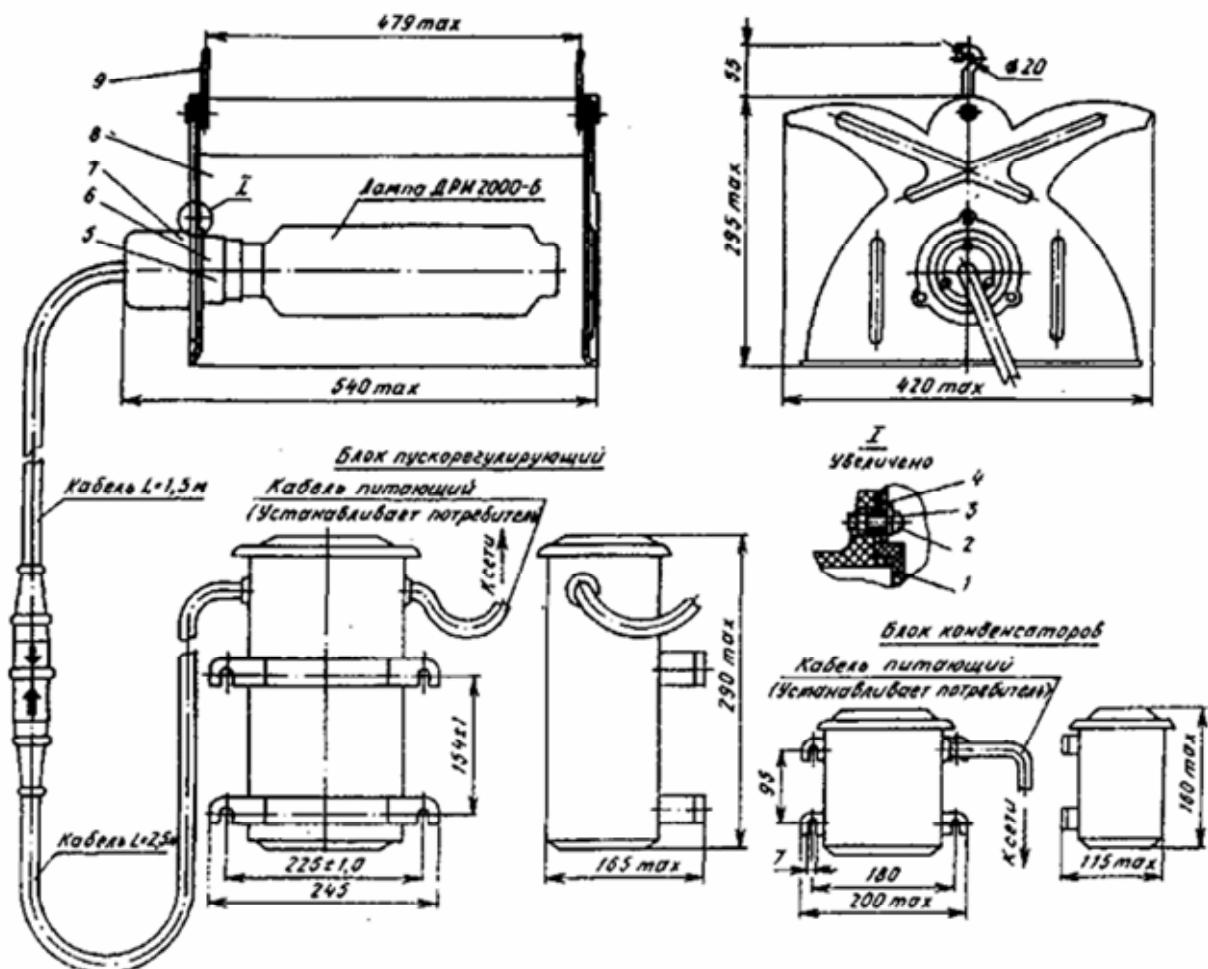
Конструкция и габаритные размеры облучателя тепличного "ФОТОС-4" типа ОГС01-2000-002 У5
